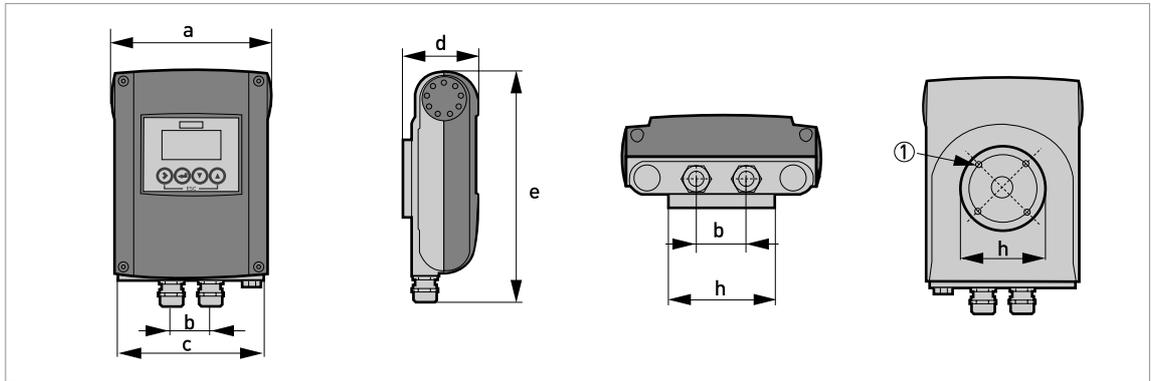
Dimensions de la version 0° compacte, boîtier en aluminium
